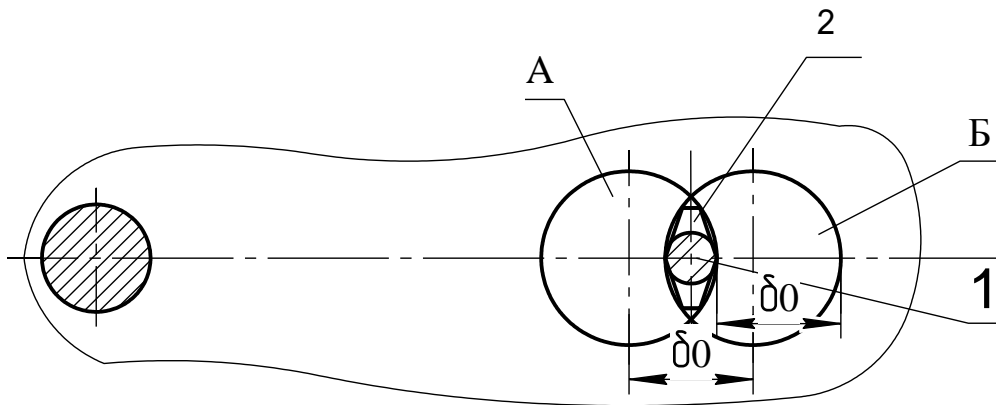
Схема установки заготовок с предельными положениями отверстий
